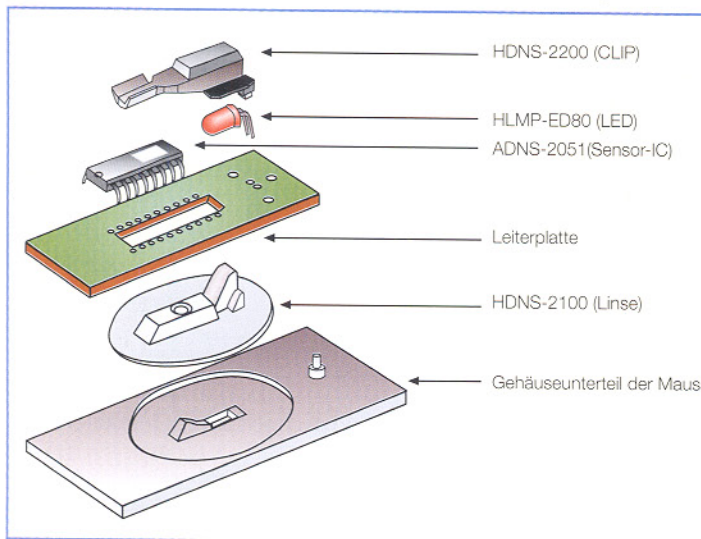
Die Explosionszeichnung verdeutlicht die mechanische Konstruktion einer optischen Maus mit dem ADNS 2051 von Agilent.
